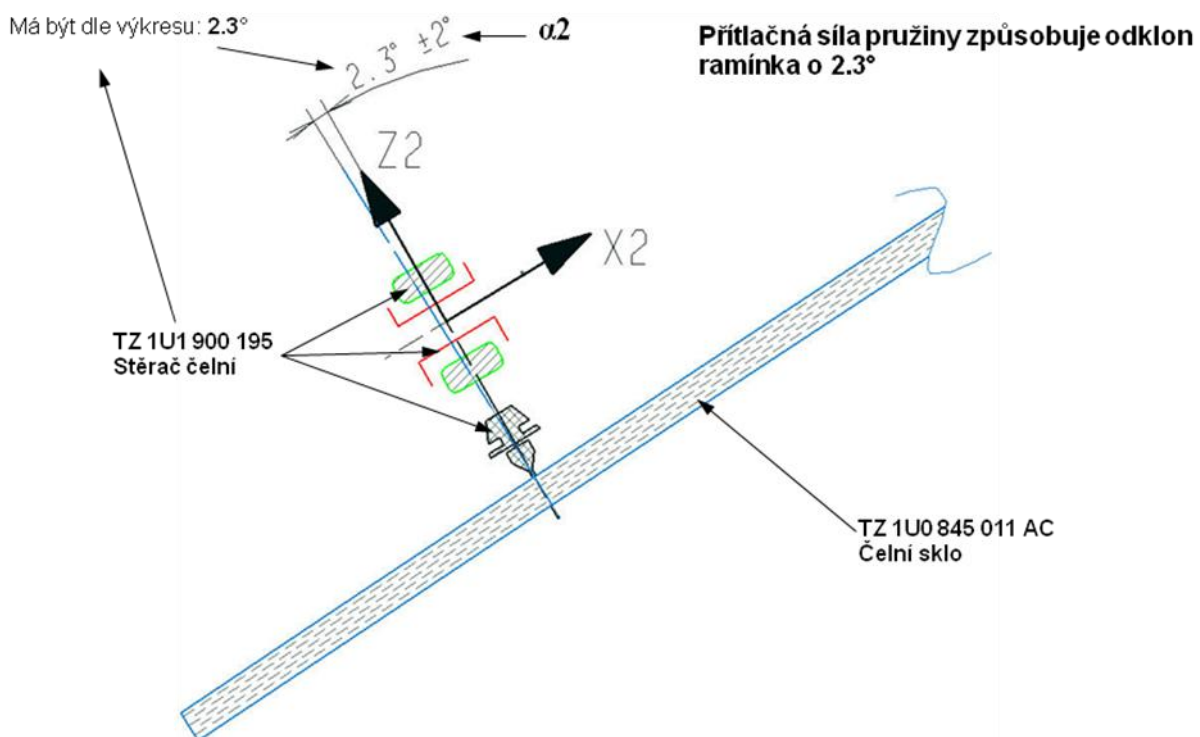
Natočení stěračové soupravy vlivem tolerance plechů – aritmetický součet tolerancí
